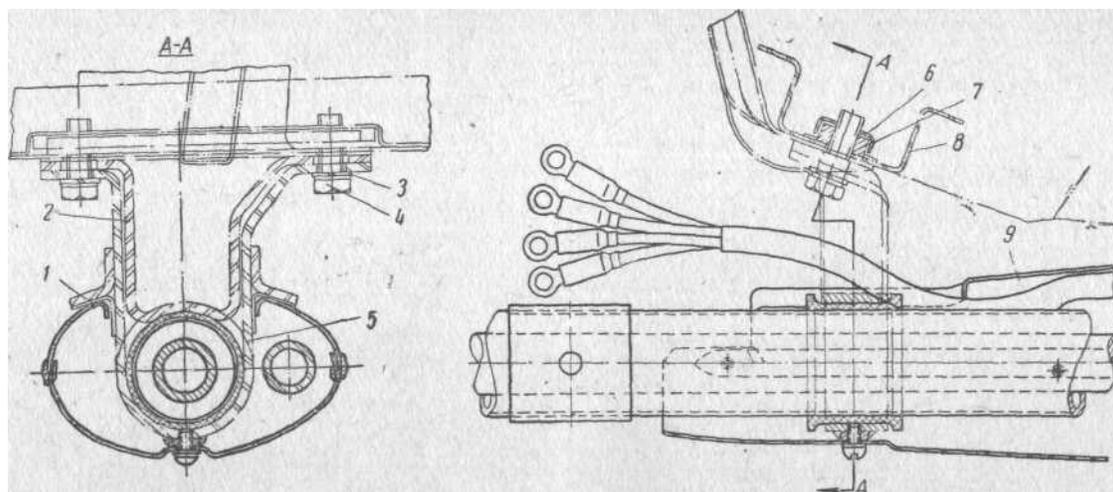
Крепление рулевой колонки автомобиля модели 407 и ее кожуха к кузову:
